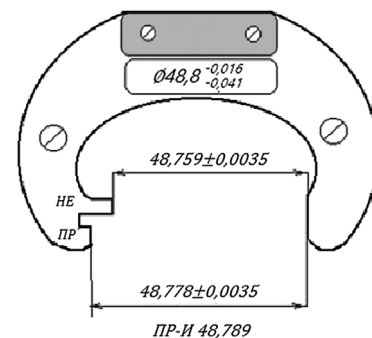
Эскиз калибра-скобы для контроля размера передней шейки промежуточного вала $\varnothing 48.8^{+0.016}_{-0.041}$ двигателей ЗМЗ
